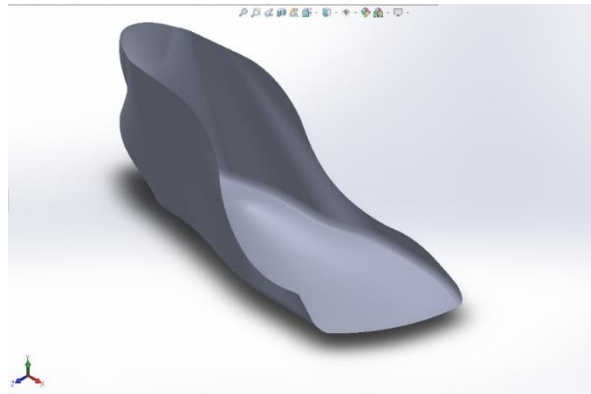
Elemento 1 conformado por la planta del pie y la sección del tobillo
